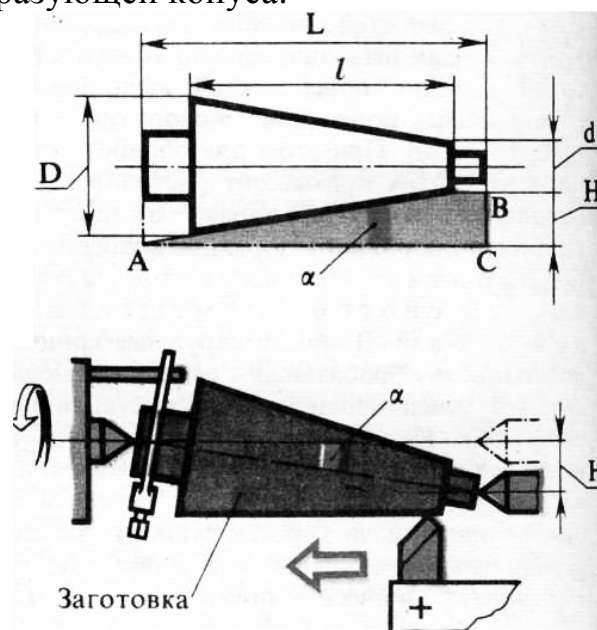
Способы обработки конической поверхности путем поворота каретки на угол конуса (верхний рисунок) и смещение задней бабки (нижний рисунок)
